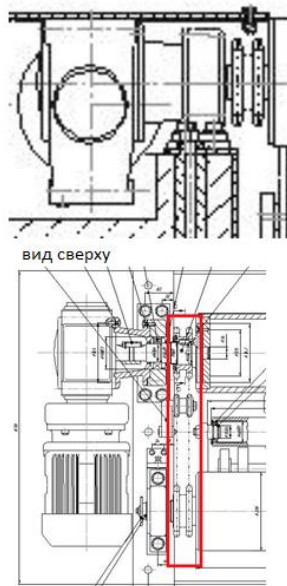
Цепная передача стандартного тормозного стенда
